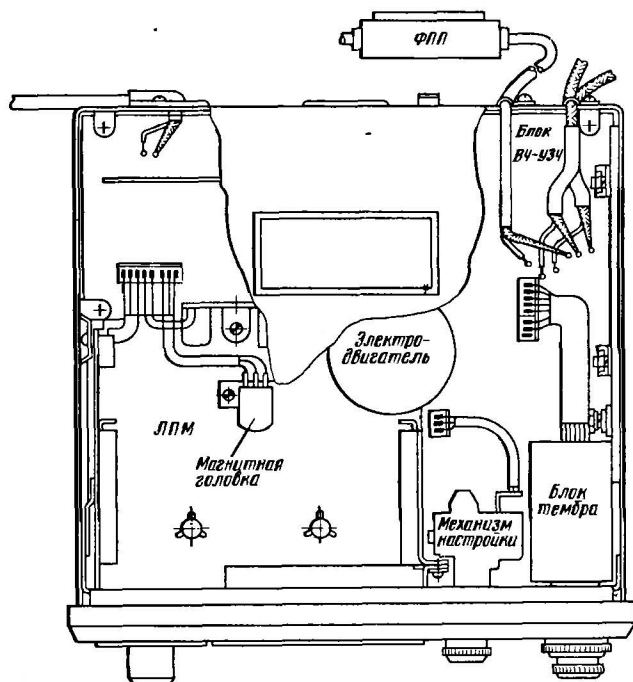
Схема расположения основных узлов и деталей в корпусе автомагнитолы «Былина РМ-317СА» (вид сверху)
